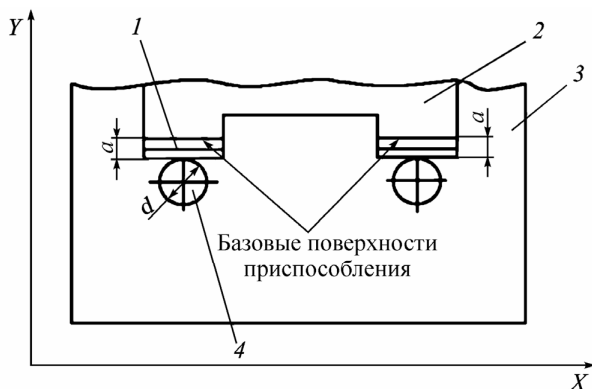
Схема выверки приспособления на столе станка по оси шпинделя с помощью мерной оправки:
